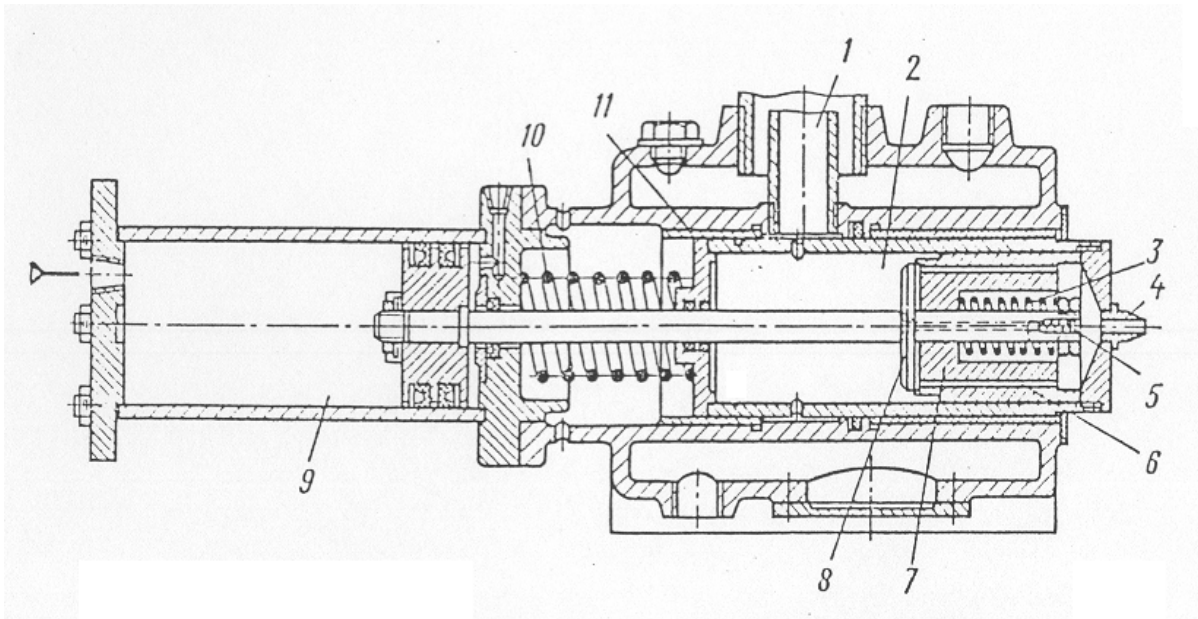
Схема устройства автоматического шприца для запрессовки пастообразных модельных составов: 1 – трубопровод; 2 – рабочая полость; 3 – пружина клапана; 4 – выпускное отверстие; 5 – обратный клапан; 6 – подводящие каналы; 7 – поршень; 8 – крышка; 9 – пневмоцилиндр; 10 – прижимная пружина; 11 – рабочий цилиндр.
